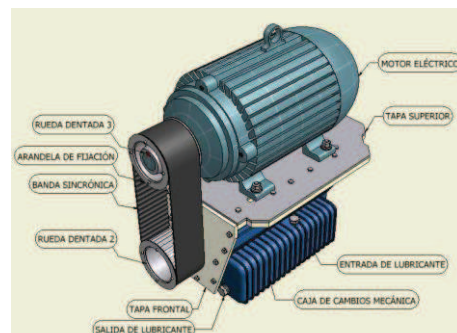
Montaje del mecanismo del motor eléctrico a la caja de cambios del Mini Austin.
